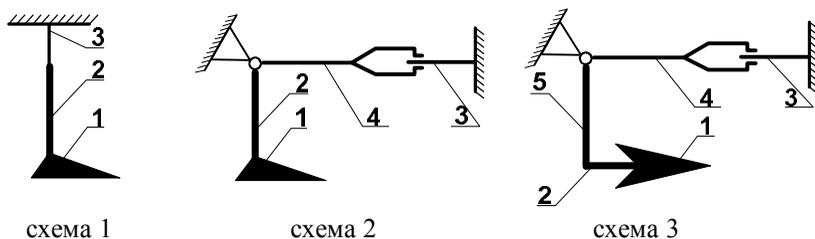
Схемы упругих подвесок лап культиватора: 1 – лапа; 2 - стойка; 3 – пружина; 4 – вилка; 5 – рычаг (плечо) вилки.
